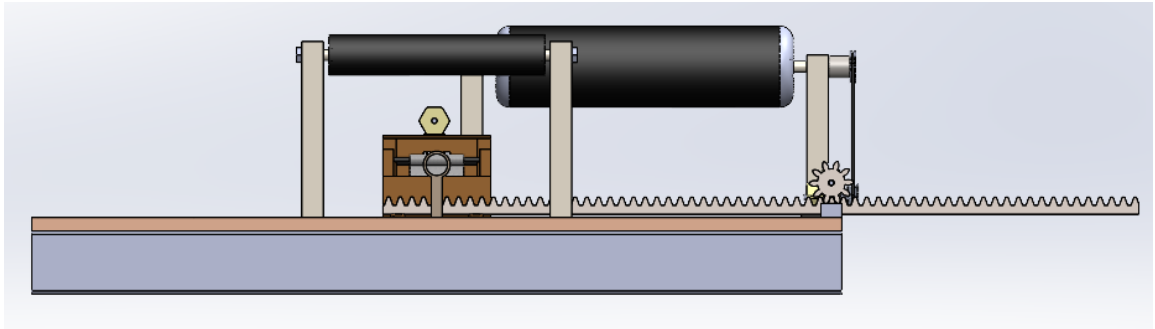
Máquina Filament Winding vista frontal. Autor
